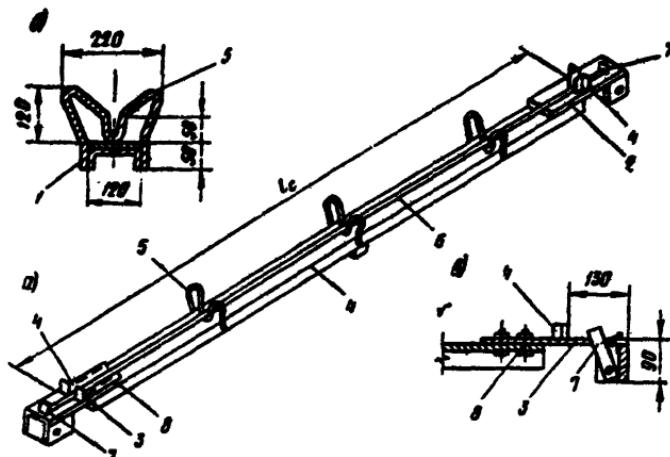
Кондуктор для приварки коротышей на концах стержней
